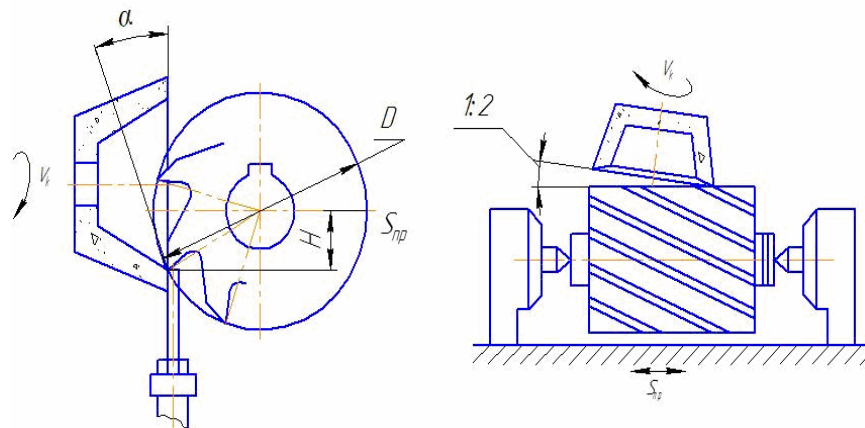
Схема заточування циліндричної фрези по задній поверхні
